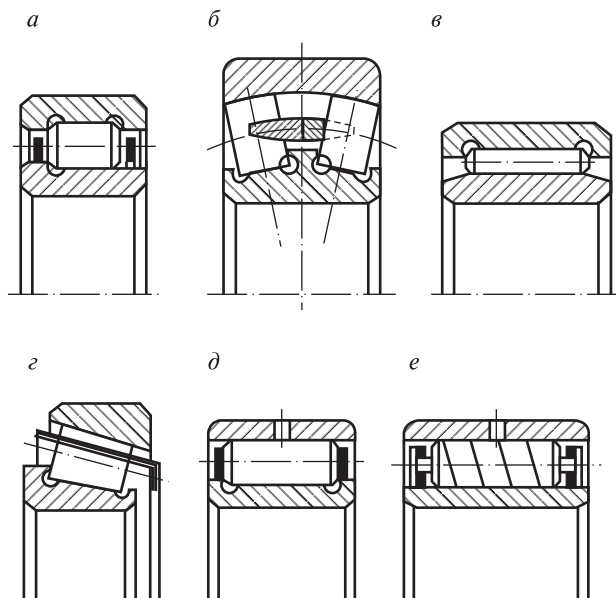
Основные типы роликоподшипников: *а* — однорядные (с короткими роликами); *б* — с бочкообразными роликами (самоустанавливающиеся); *в* — игольчатыми роликами; *г* — конические; *д* — однорядные (с длинными роликами); *е* — однорядные (с витыми роликами)
